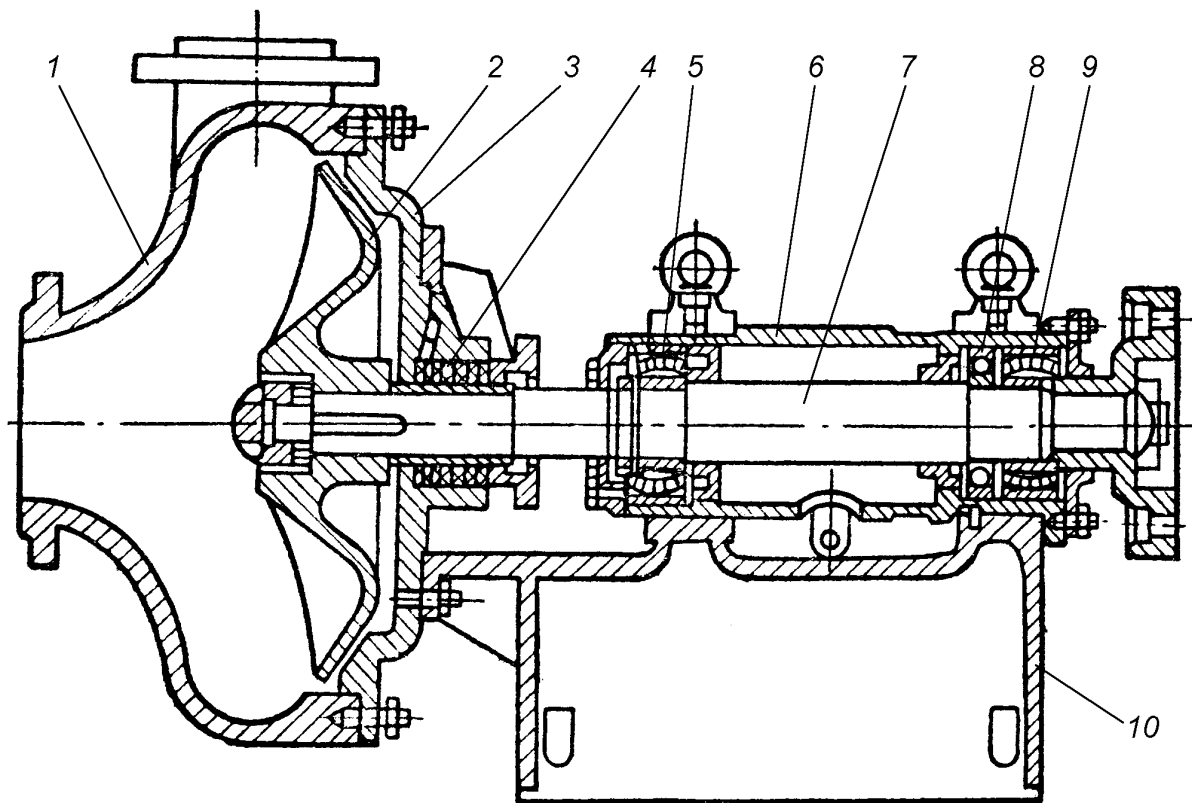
«Смерчковий» насос: 1 – корпус; 2 – робоче колесо; 3 – задня кришка; 4 – сальник; 5, 9 – радіальні роликопідшипники; 6 – стакан; 7 – вал; 8 – радіально-упорний шарикопідшипник; 10 – станина
